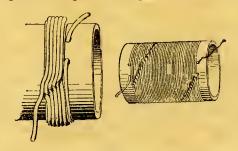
Способ намотки и общий вид готовой двуслойной катушки.
